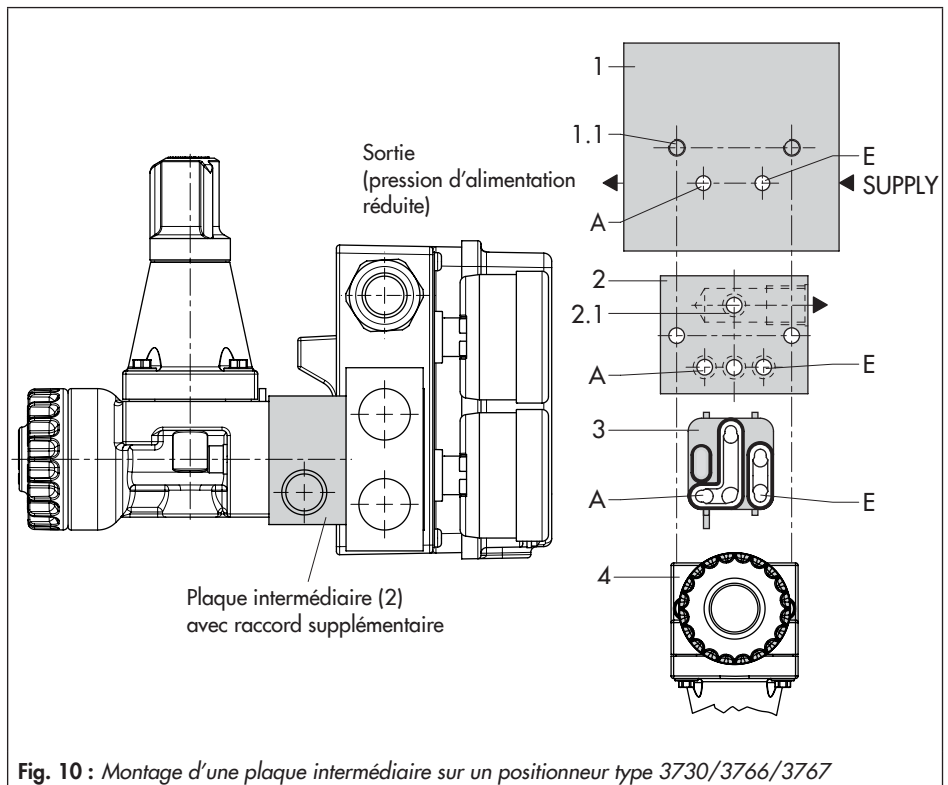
Montage d'une plaque intermédiaire sur un positionneur type 3730/3766/3767
